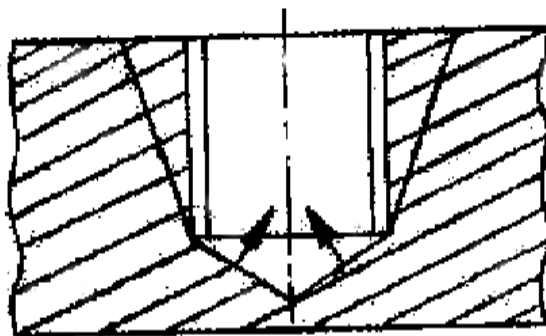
Подготовка к заварке резьбовых отверстий
